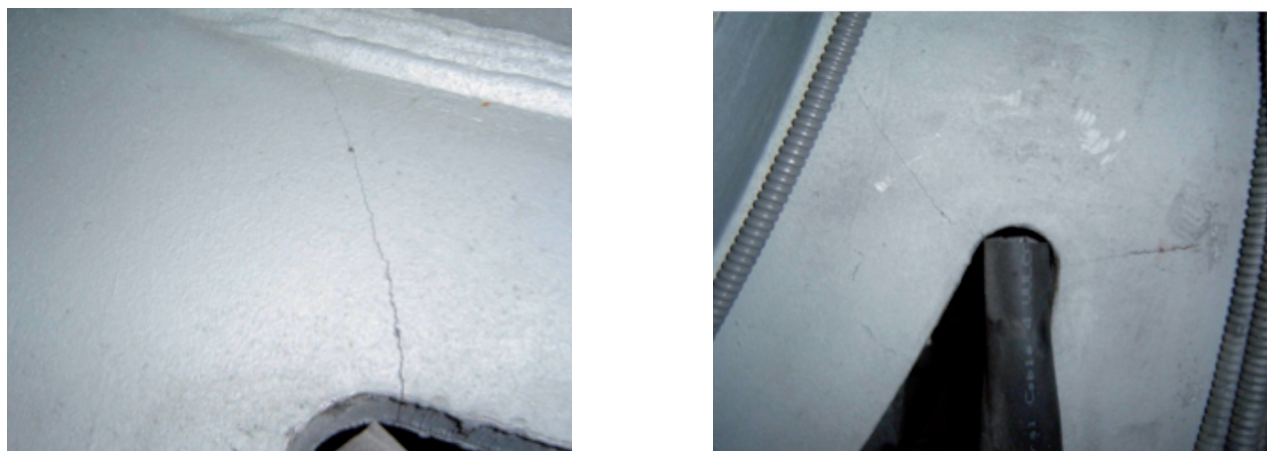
Detalle grietas por fatiga en bastidor de MADE AE61.
